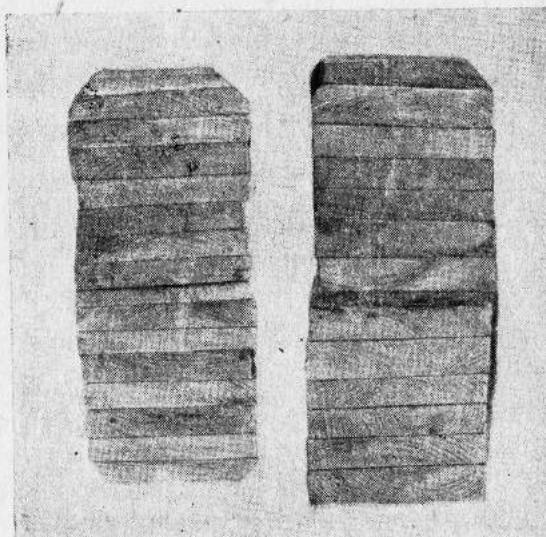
Обрезка припусков для изготовления контрольных образцов
